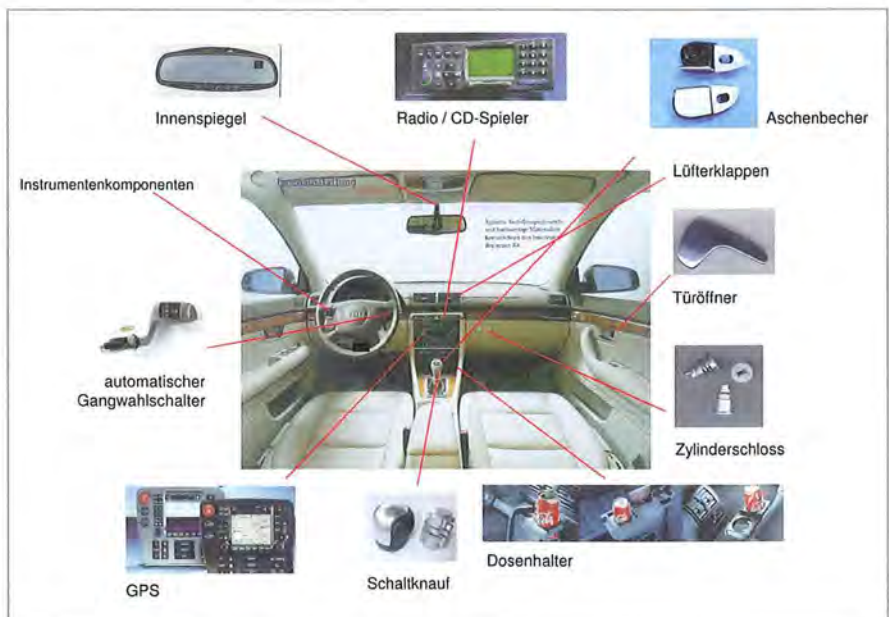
Zinkdruckgussteile im Automobil (Innenraum)
